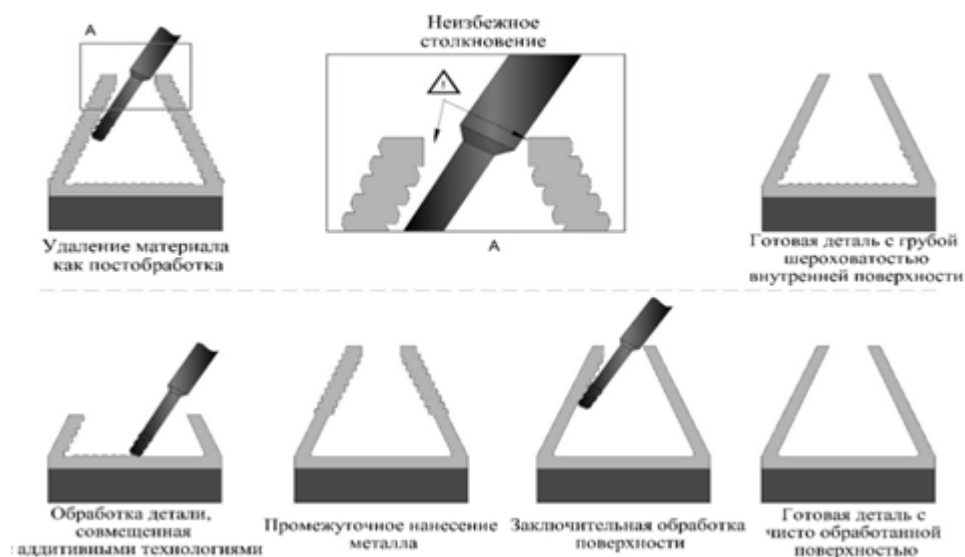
Проблемы, связанные с операцией фрезерования выращенной заготовки
